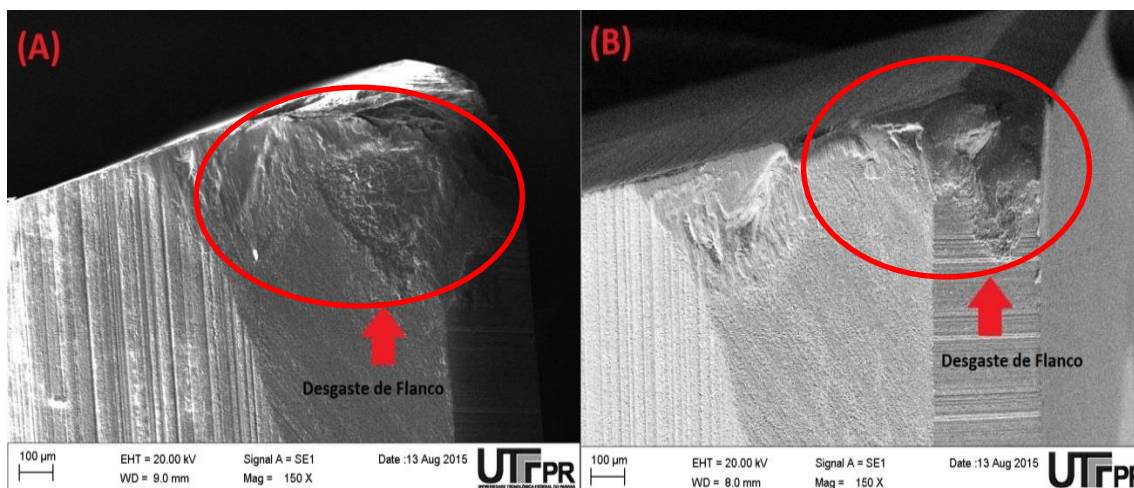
MEV das ferramentas utilizadas nos ensaios com a condição de usinagem F_2 com fluido de corte mineral: (A) fluido novo; (B) fluido tratado
